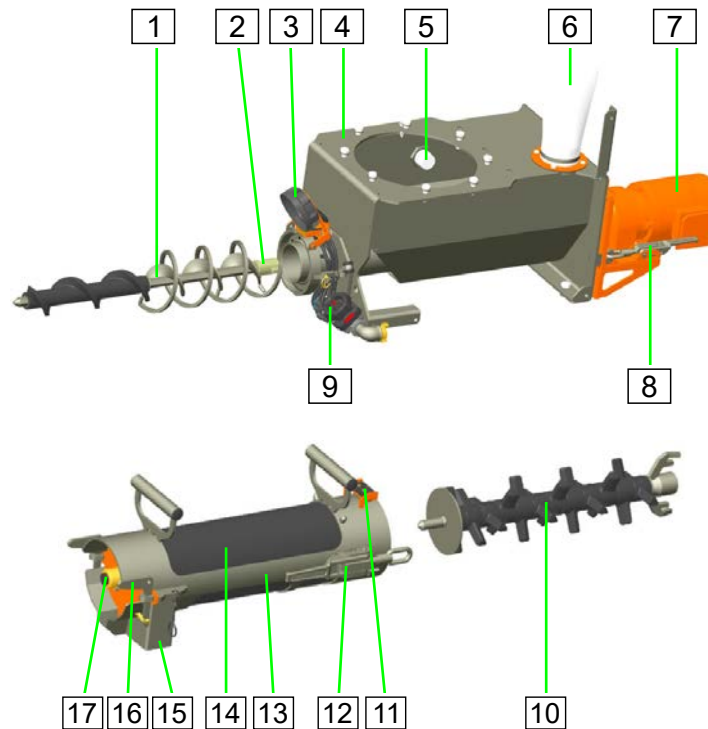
Baugruppe Mittelkörper mit Mischrohr
